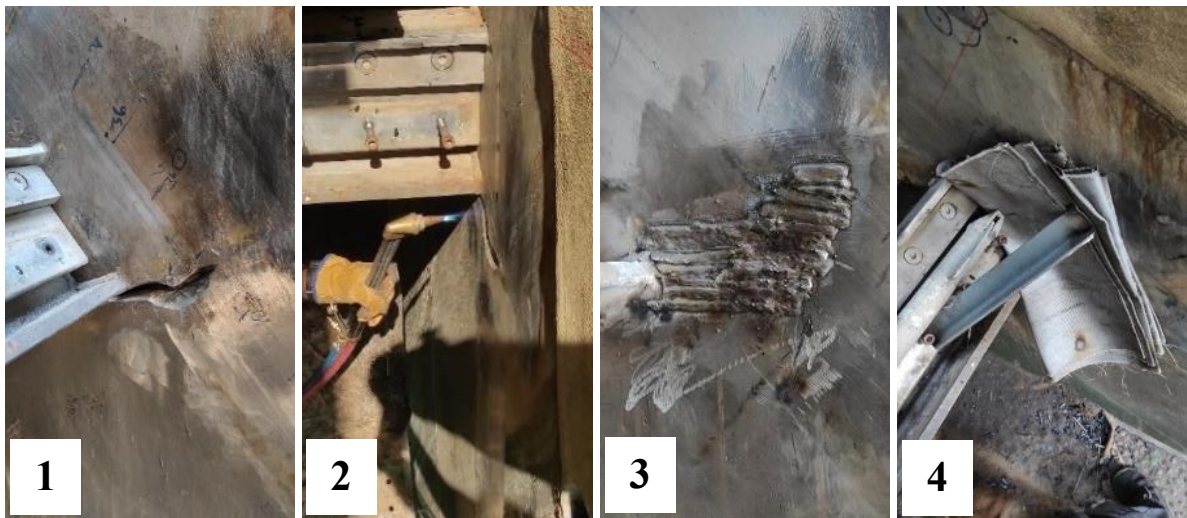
Fissura DC1 – detalhe da fissura com cerca de 11cm de comprimento a começar na soldadura da travessa frontal com a peça fixa lateral
